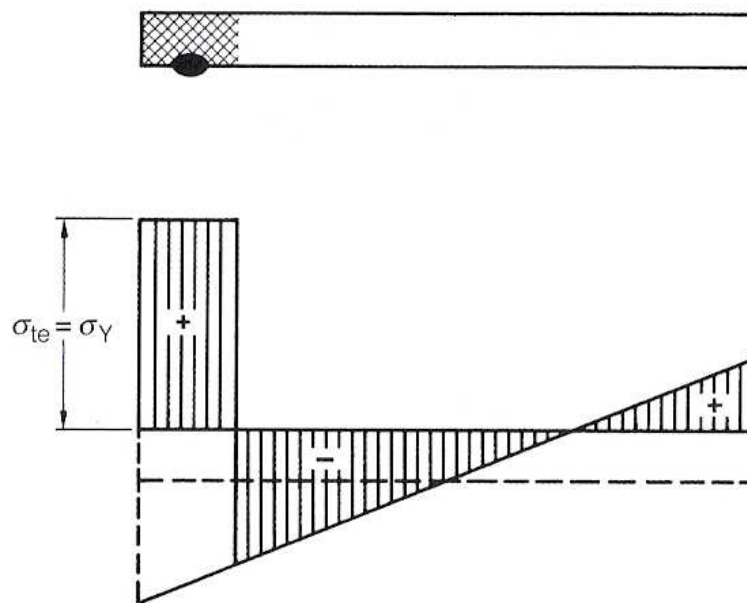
Esfuerzos residuales longitudinales en una placa rectangular sin restricción con una soldadura longitudinal excéntrica ¹¹
